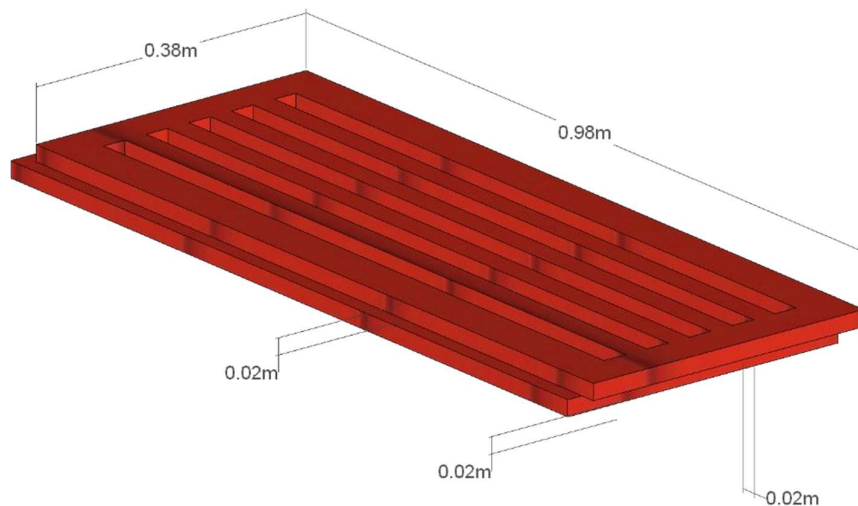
Vista inferior de plancha - Parte No.1 del proyecto.
